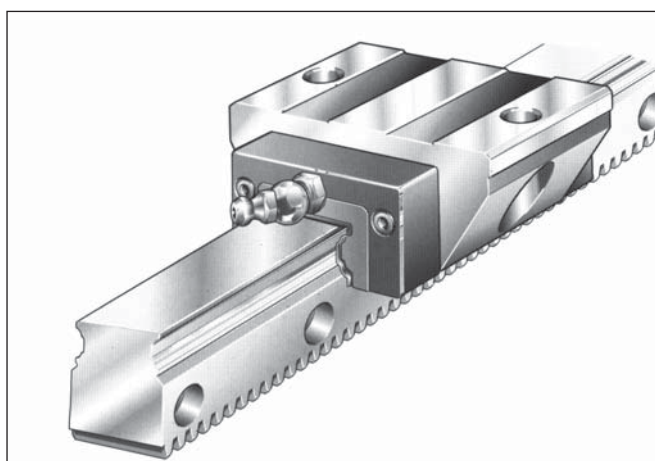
Внешний вид РНК с кареткой INA серии TKVD с зубчатой нижней поверхностью.
